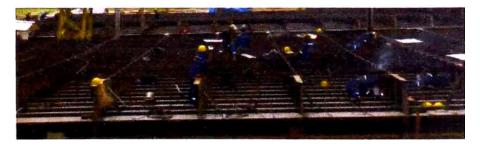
Longitudinales de Cubierta de Doble Fondo
